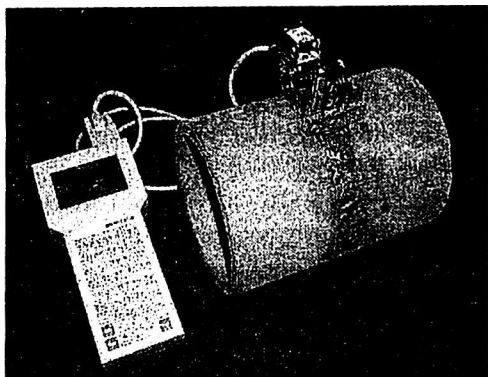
Схема контроля стыковых сварных соединений труб четырехканальным датчиком прибора ИКН-1М-4:
